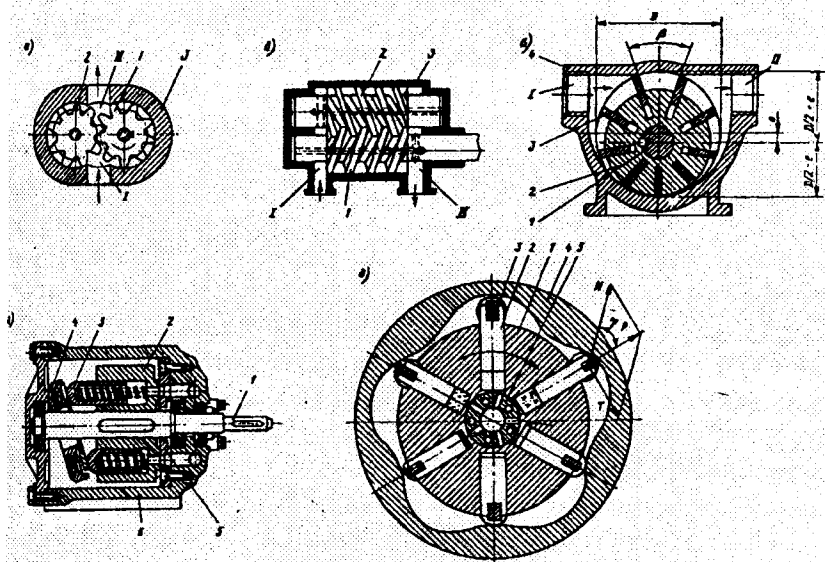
Конструктивные схемы насосов и гидромоторов:
